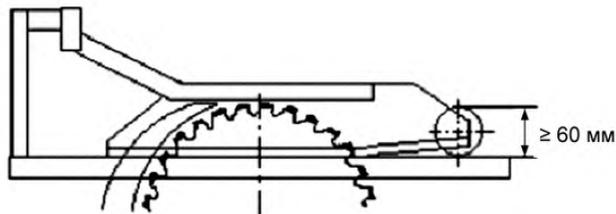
б) – Регулируемый кожух дисковой пилы с вталкивающими роликами
